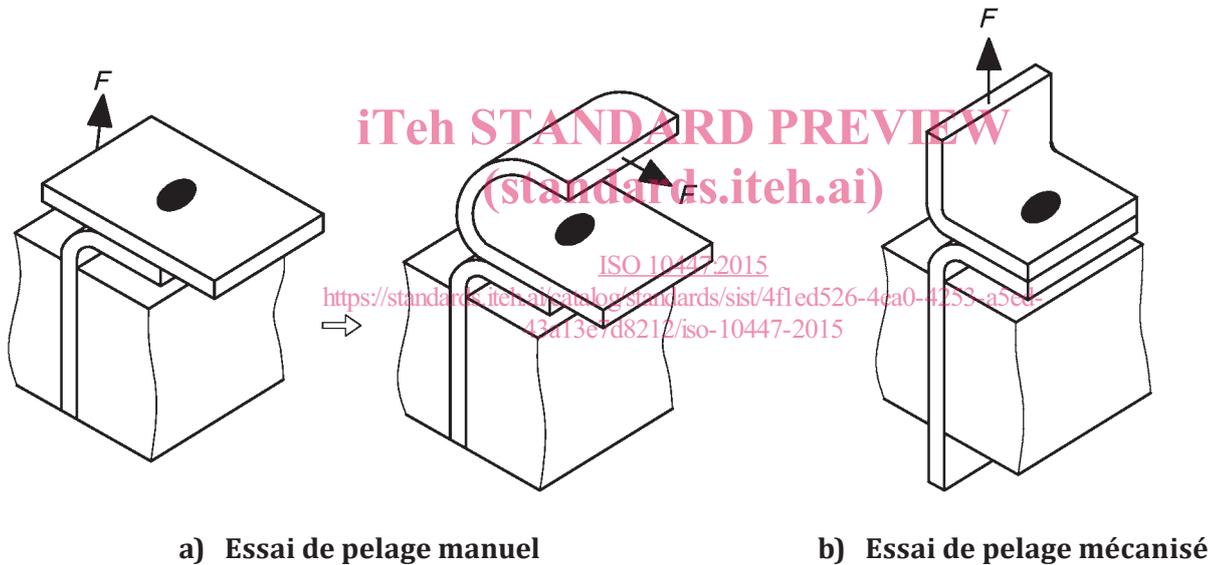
Essai de pelage sur joints soudés par résistance par points et par bossages
